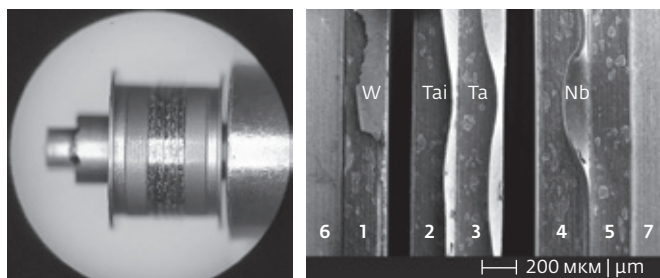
Слева: общий вид катодной сборки; справа: РЭМ-изображение сборки
